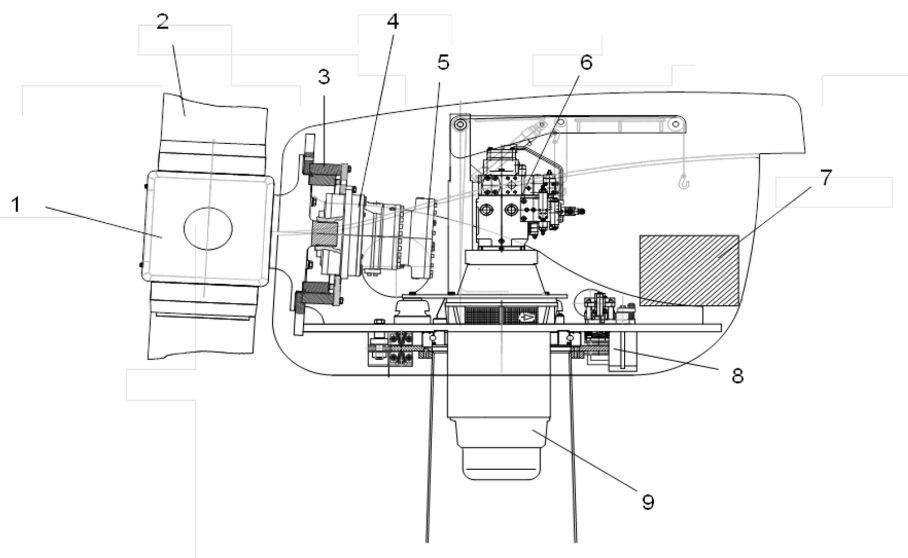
Компонка ветроэнергетической установки NordWind (вид мотогондолы сбоку): 1 – ступица; 2 – лопасть ротора; 3 – подшипник ротора; 4 – насос; 5 – аварийный тормоз; 6 – гидравлический двигатель; 7 – блок управления; 8 – тормоз по азимуту; 9 – генератор
